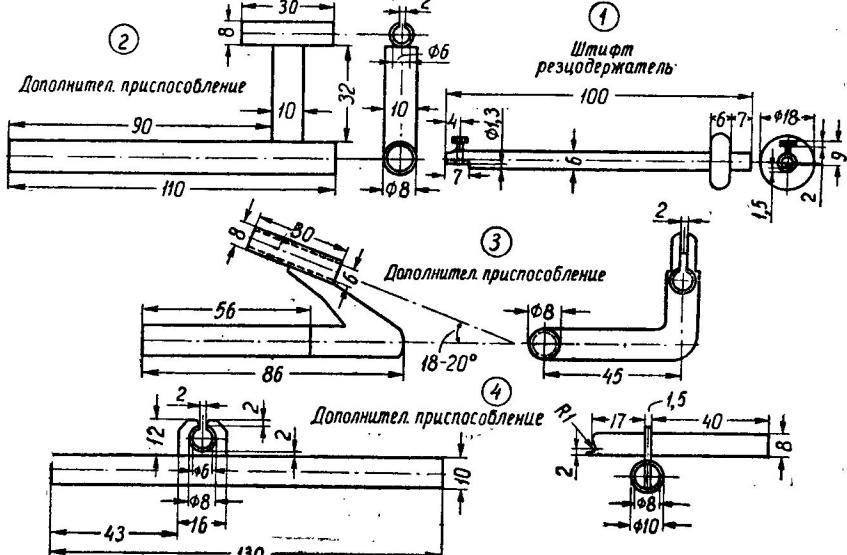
Штифт-резцедержатель и дополнительные приспособления
